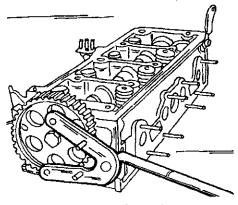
Отворачивание болта зубчатого шкива распределительного вала. Удерживать зубчатый шкив указанным образом.
